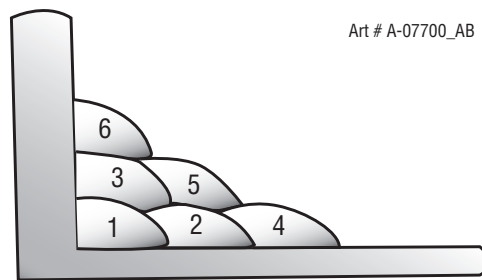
Plusieurs passages d'une soudure d'angle HV
